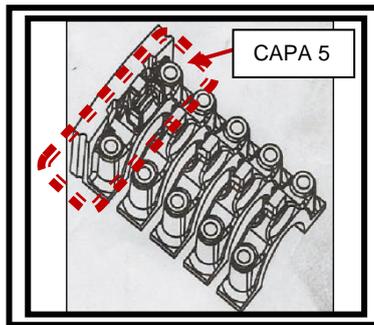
DESENHO DA PEÇA APÓS USINAGEM
